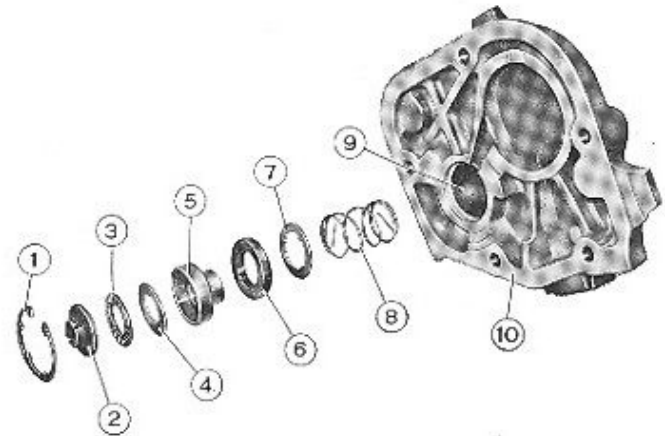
Arbeitszylinder zur Betätigung der hydraulischen Ausrückvorrichtung.
